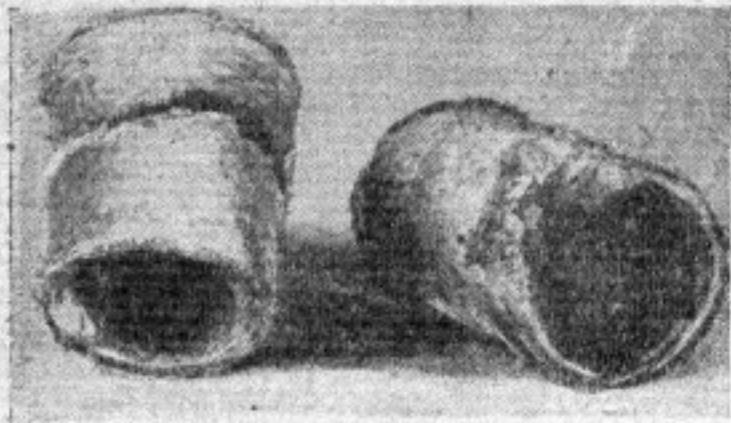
Обрыв соединительного резино-асбестового шланга патрубка отбора газа
